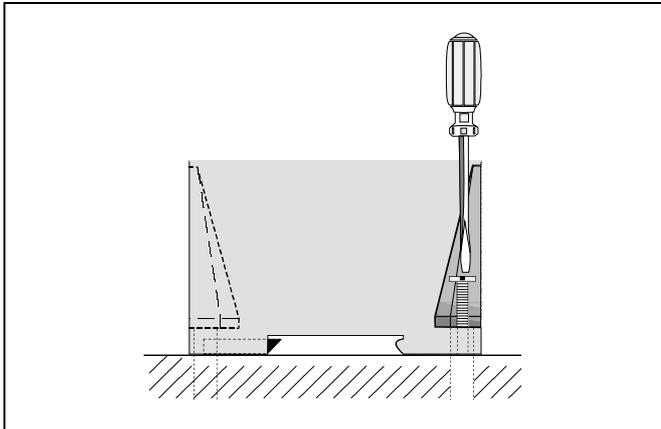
Demontage bei Befestigung mit zwei M4-Schrauben
